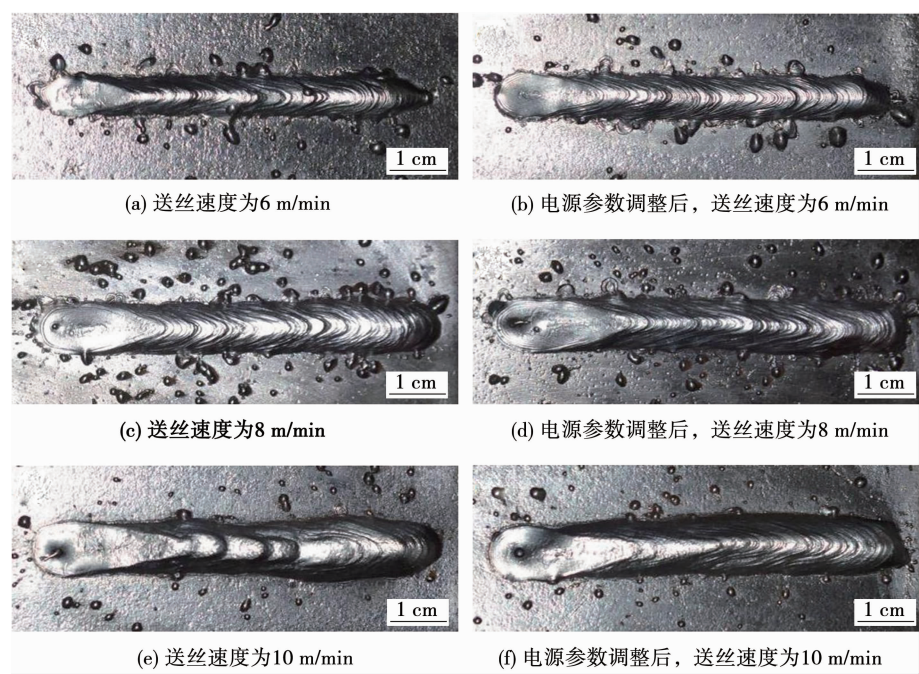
焊接电源控制参数调整前后获得的焊缝形貌
